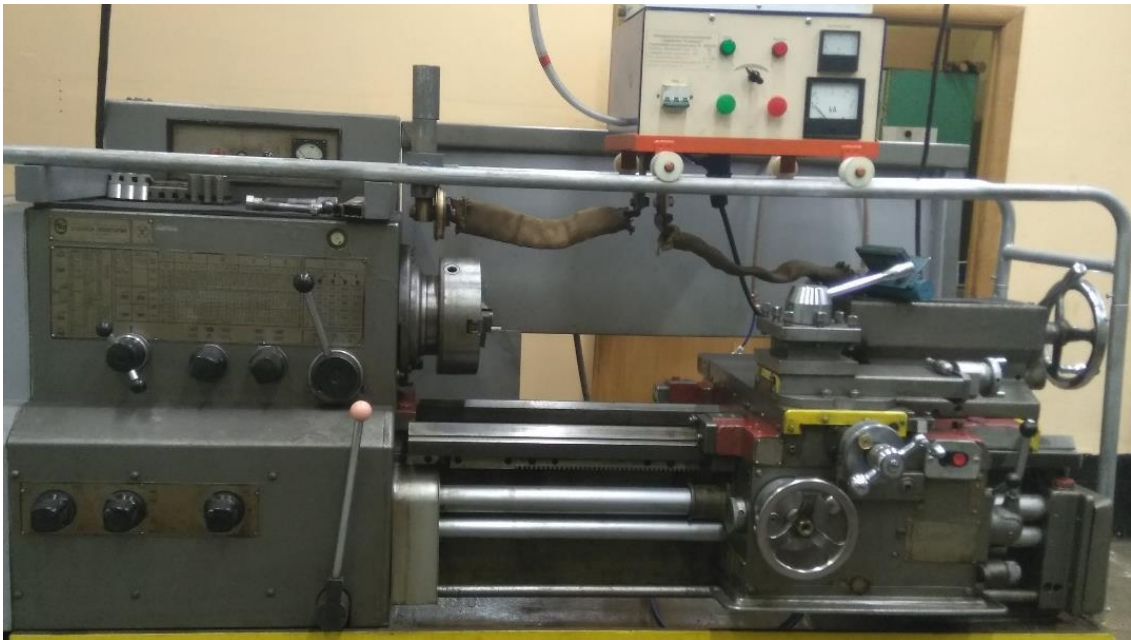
Токарно-гвинторізний верстат для електромеханічної обробки.
